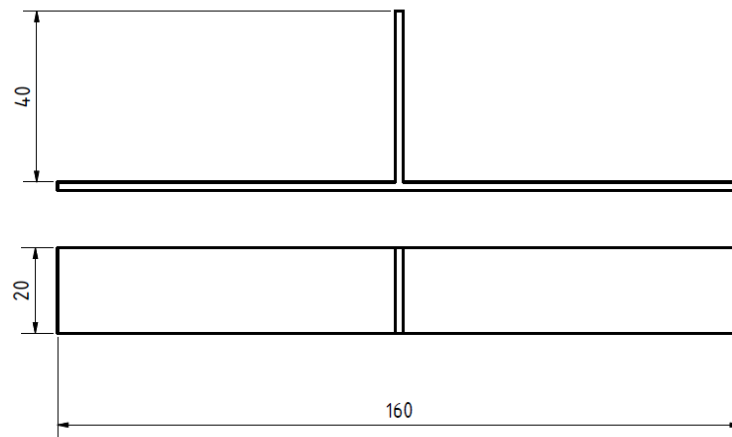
Geometria do provete para ensaio de tração (dimensões em mm)
